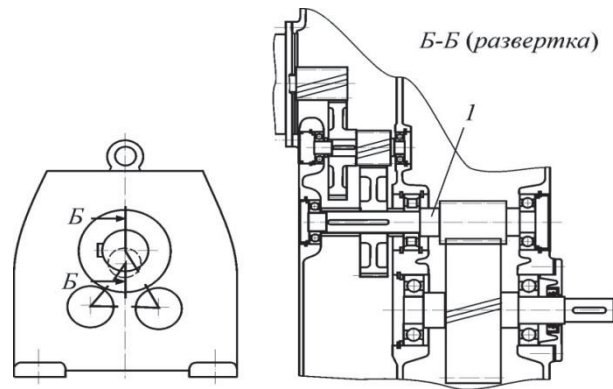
Вид спереди на мотор-редуктор фирмы SEW Eurodrive и развертка его по осям валов для случая трехступенчатого исполнения
